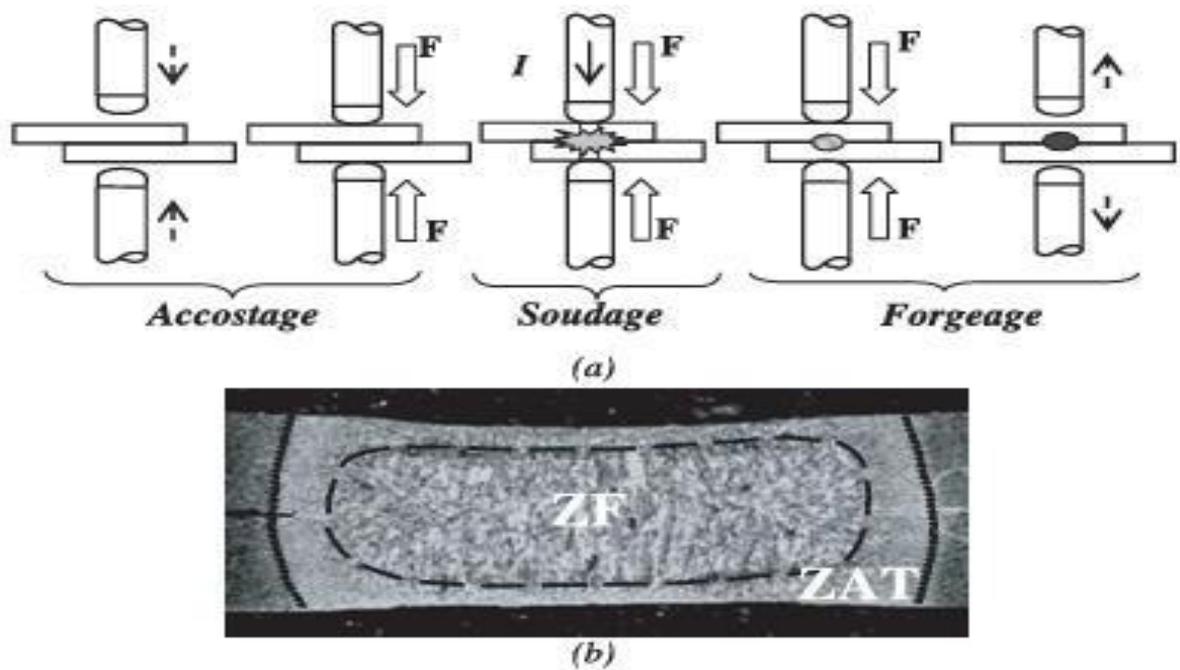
(a) Principe du soudage par résistance. (b) Exemple de zone fondue
